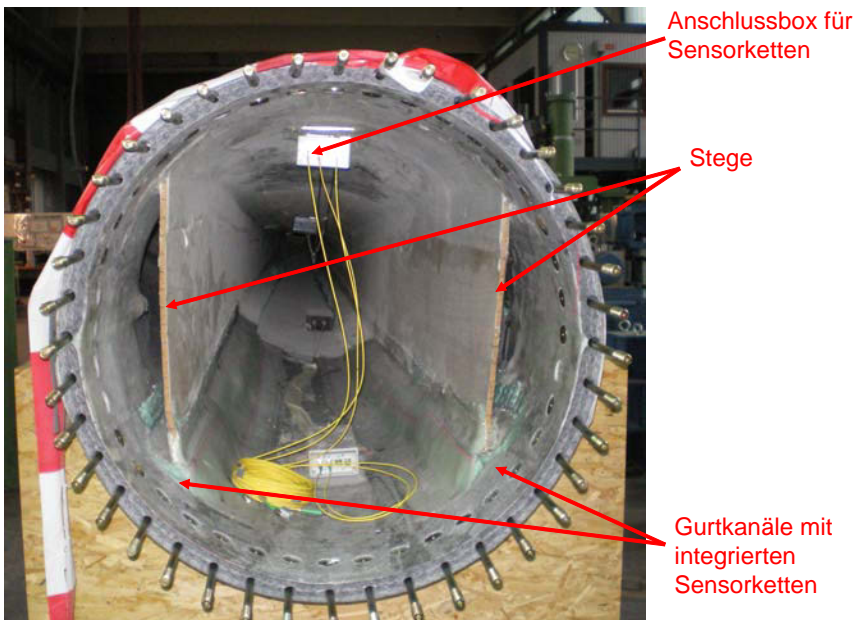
Blick auf die Innenseiten des Stellvertreter-Rotorblatts mit den Anschlussboxen der Sensorketten. Die Sensorketten sind in den vier Gurtkanälen integriert, auf denen die beiden Stege aufgeklebt wurden.
